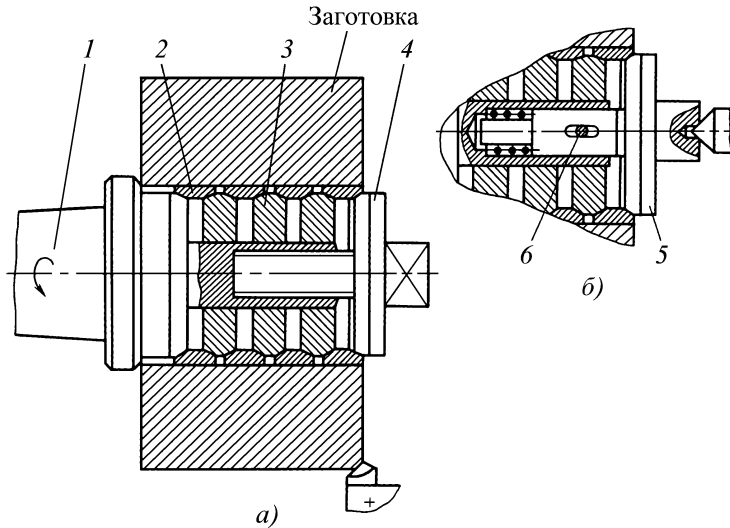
Оправка с разжимными кольцами для закрепления втулок:
